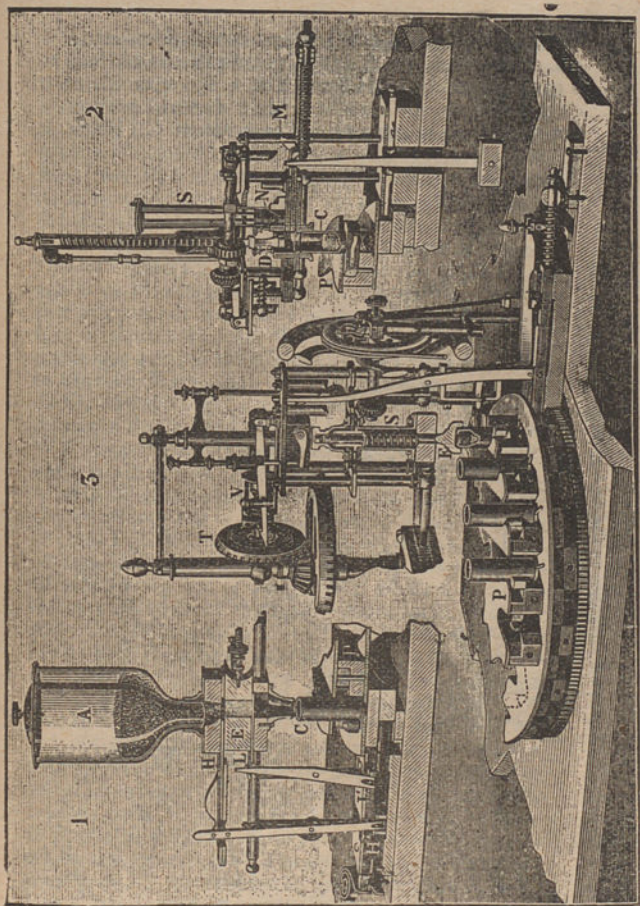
Detalhes da machina de fazer cartuxos de polvora para caça
